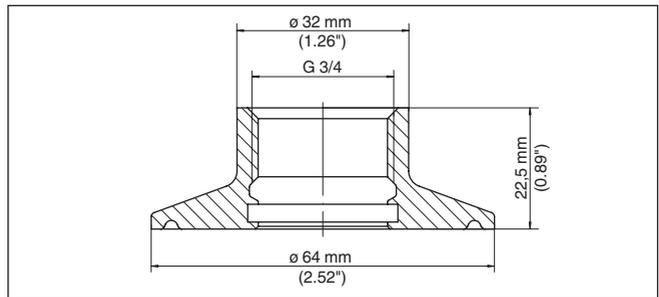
Dimensiones adaptador de rosca G $\frac{3}{4}$ (DIN 3852-X) a Clamp 2" (DIN 32676, ISO 2852) PN 16
